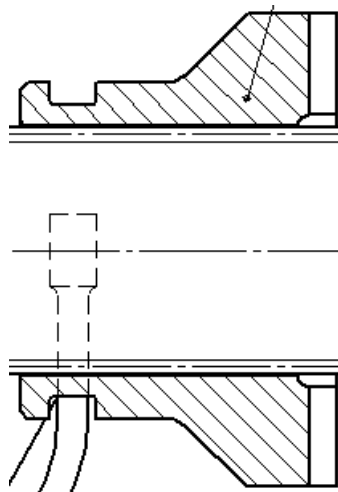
Общий вид шлицевого соединения полумуфты блокировки межколесного дифференциала и вала дифференциала
